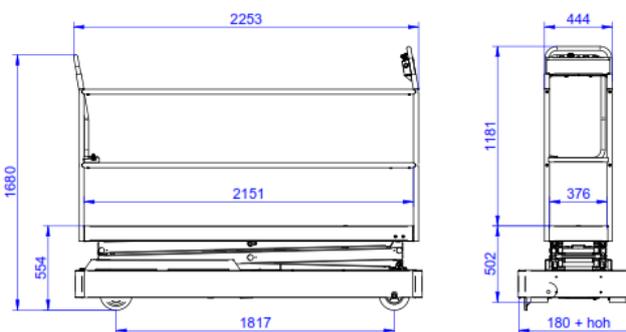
Dimensiones mínimas de la carretilla de 2 tijeras hasta 3,5 metros
